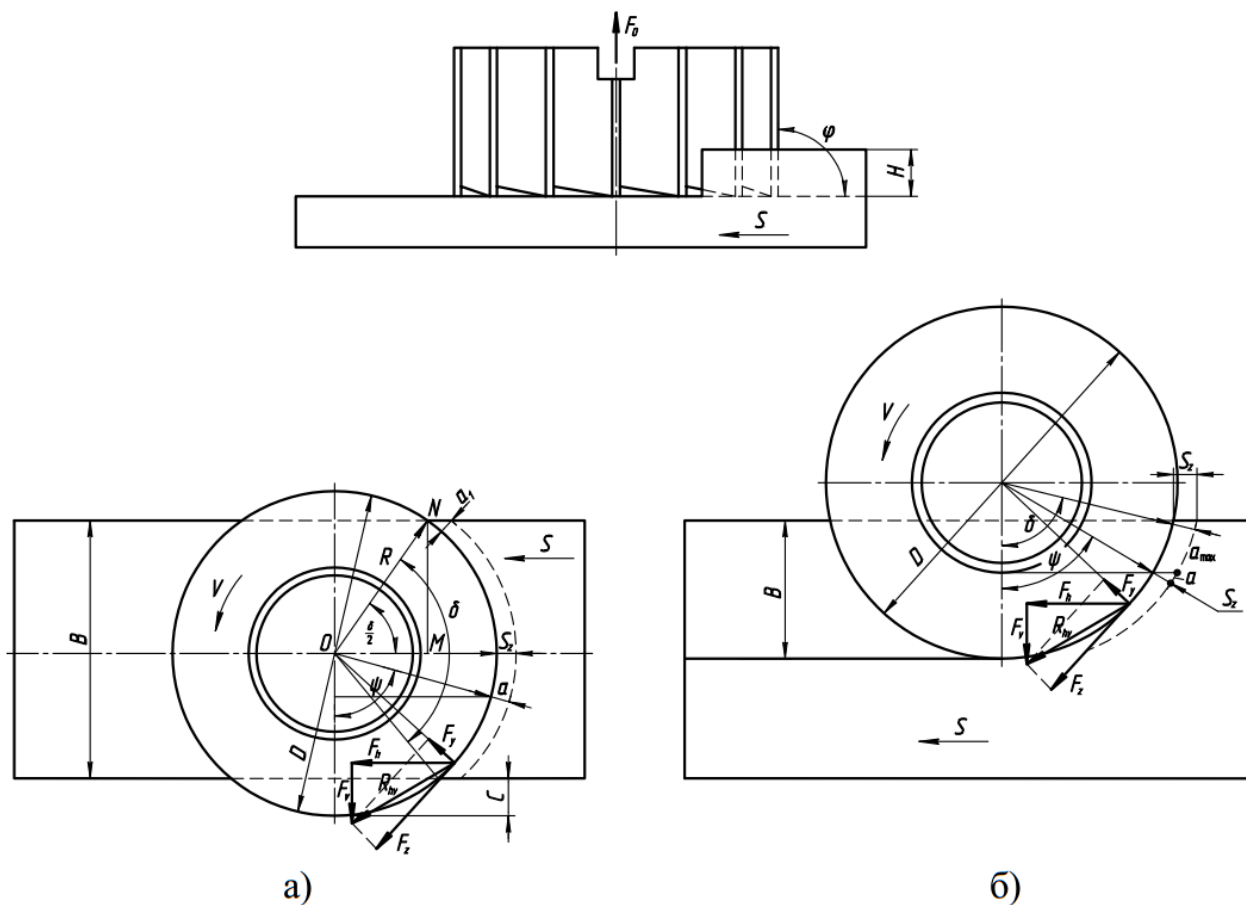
Елементи і сили різання при торцевому фрезеруванні:
